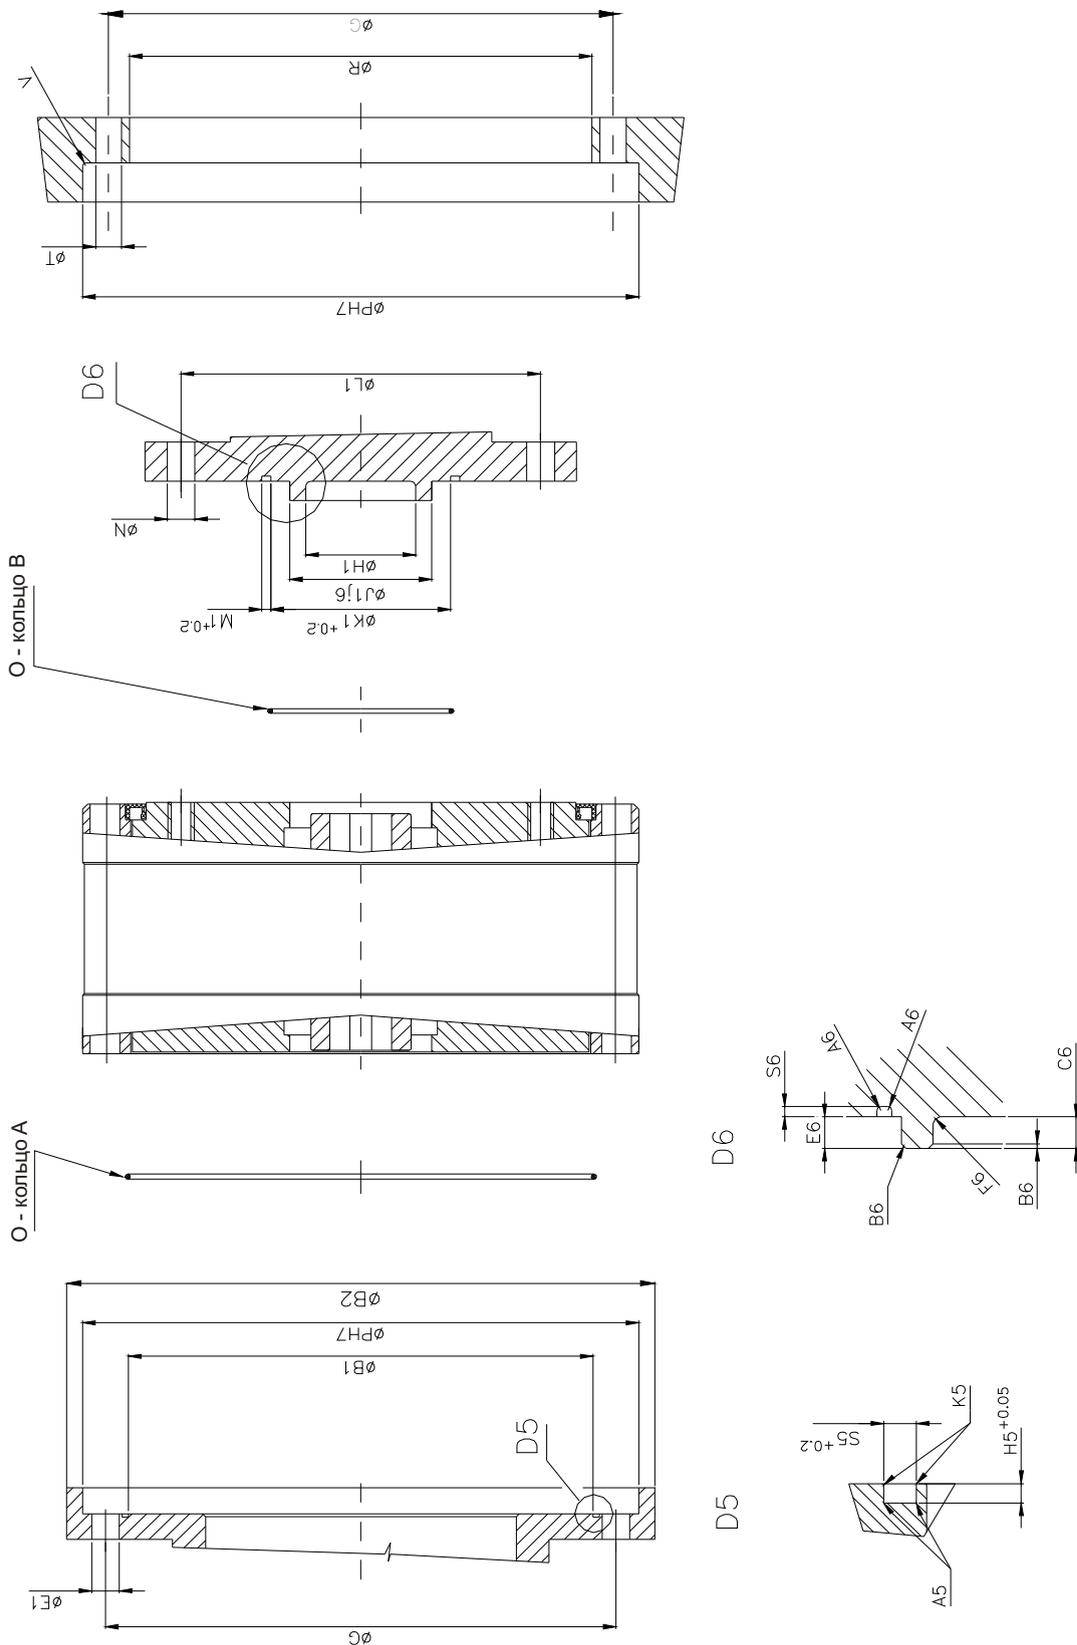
Dimensions for input and output flanges of TwinSpin bearing reducer model T up to TS 240,300/
